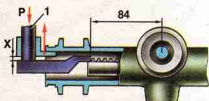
Проверка зазора между упором рейки и гайкой: 1 – пунсон; X – контрольный размер
